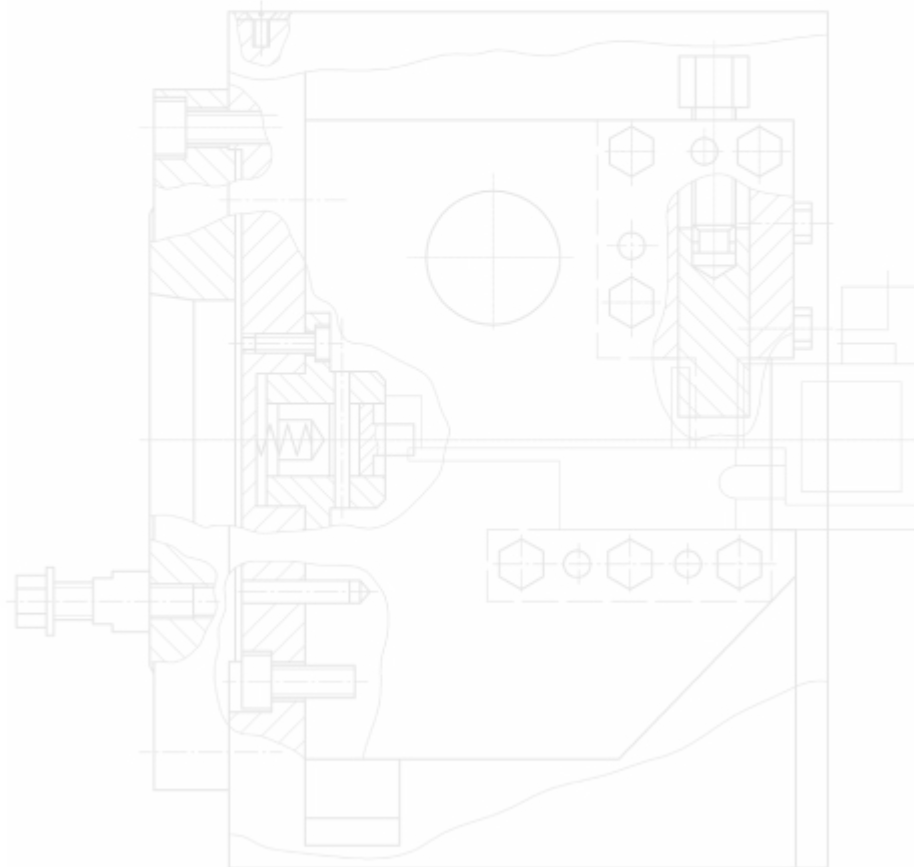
Пристрій для токарного оброблення корпусу
